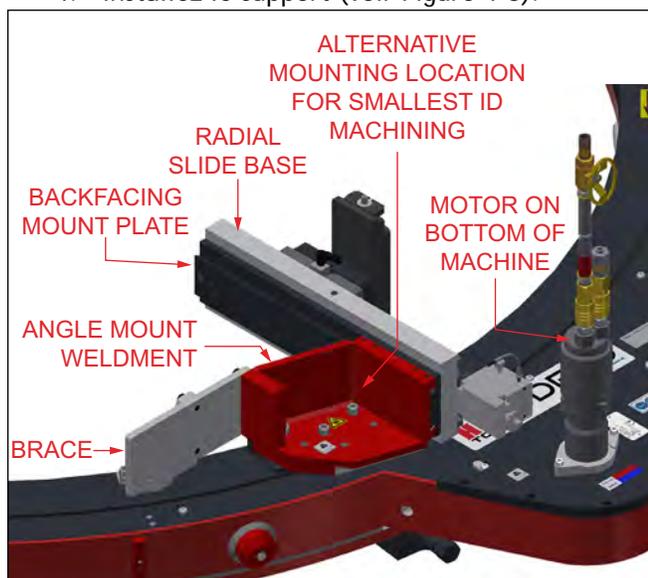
NOUVEL EMPLACEMENT DU MOTEUR ET EMPLACEMENT DU SUPPORT (ILLUSTRATION AVEC LA ODF80)
